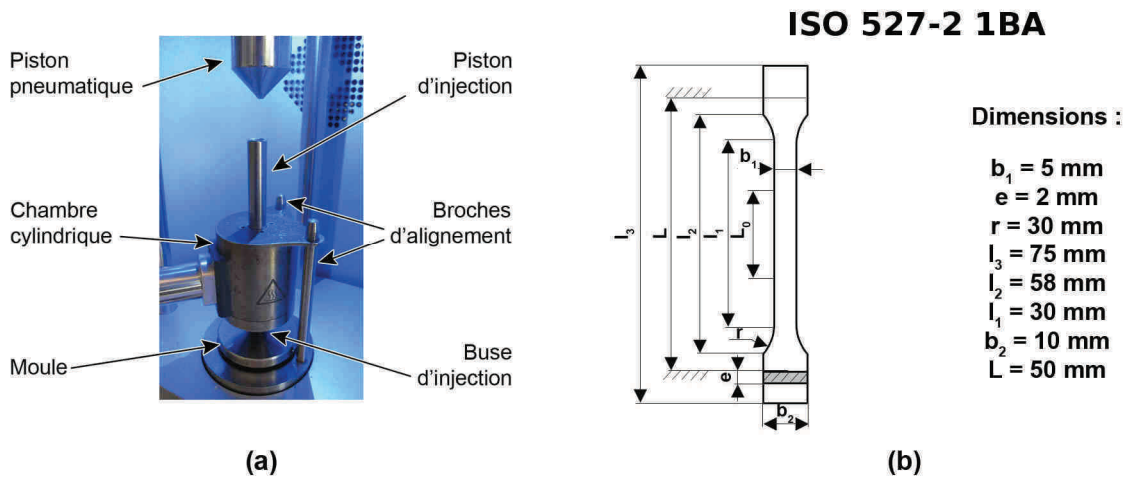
Description de la presse MiniJet II (a) et dimensions des éprouvettes aux normes ISO 527-2 1BA (b)
